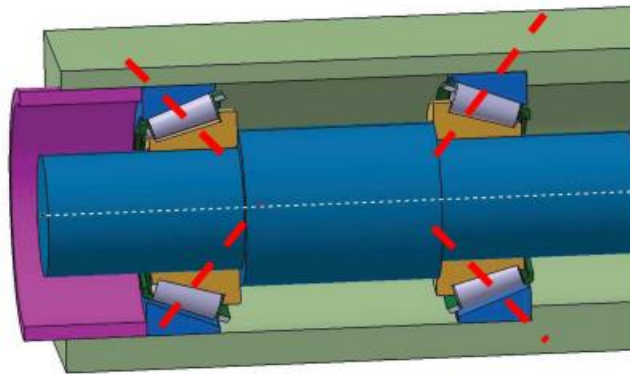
esquema de un montaje típico de rodamientos de rodillos cónicos en x
